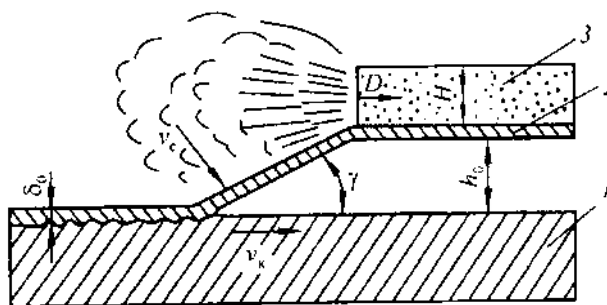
Схема зварювання вибухом плоских двошарових заготовок.
